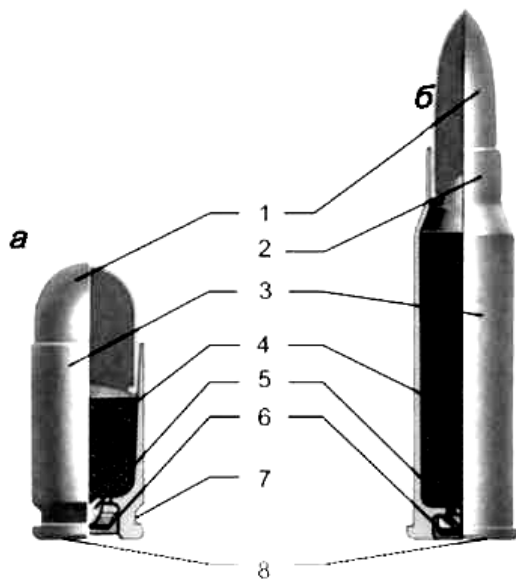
Устройство патронов к ручному нарезному стрелковому оружию: 1 – пуля; 2 – дульце; 3 – гильза цилиндрической (а) и бутылочной (б) формы; 4 – пороховой заряд; 5 – затравочное отверстие; 6 – капсюль; 7 – кольцевая проточка; 8 – наковальня
